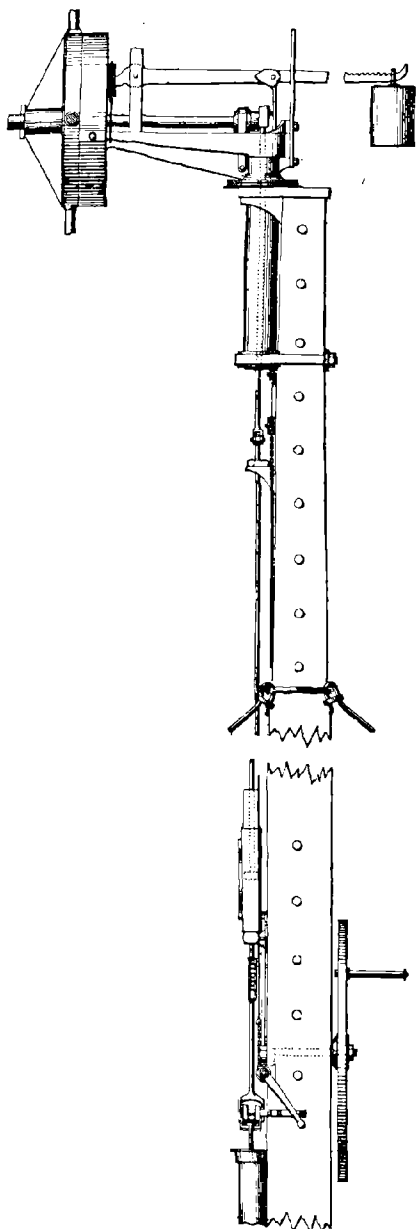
Moulin à vent Amédée Durand (vue d'ensemble).
